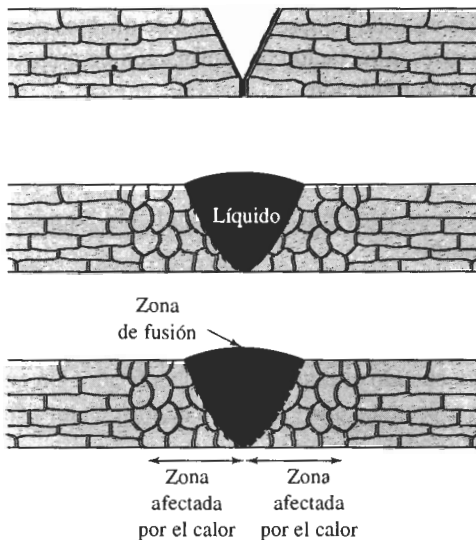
Diagrama esquemático de la zona de fusión y de la solidificación durante la soldadura por fusión: (a) Unión preparada para la soldadura, (b) soldadura a su temperatura máxima, con la unión llena de metal de aporte en estado líquido y (c) soldadura después de la solidificación.
